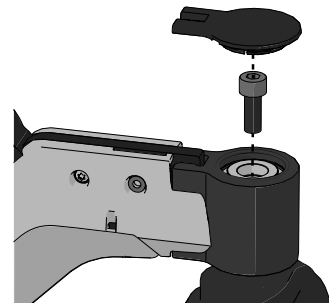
Entfernen Sie die Abdeckung und lösen Sie die Schraube.
